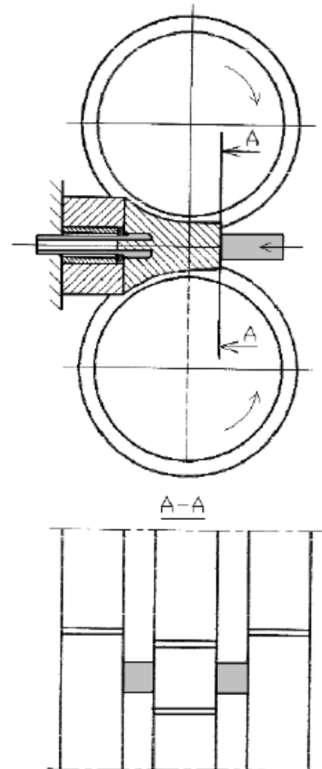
Універсальний пристрій для одержання прес-виробів різної форми
